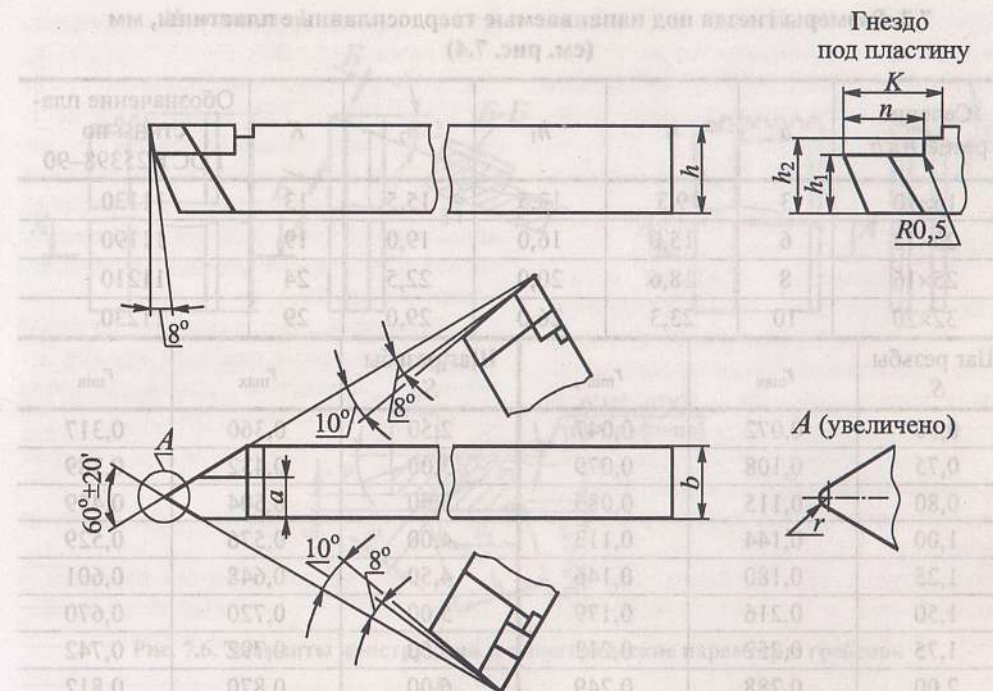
Размеры гнезда под твердосплавные пластины резцовых резцов для нарезания наружных резьб
